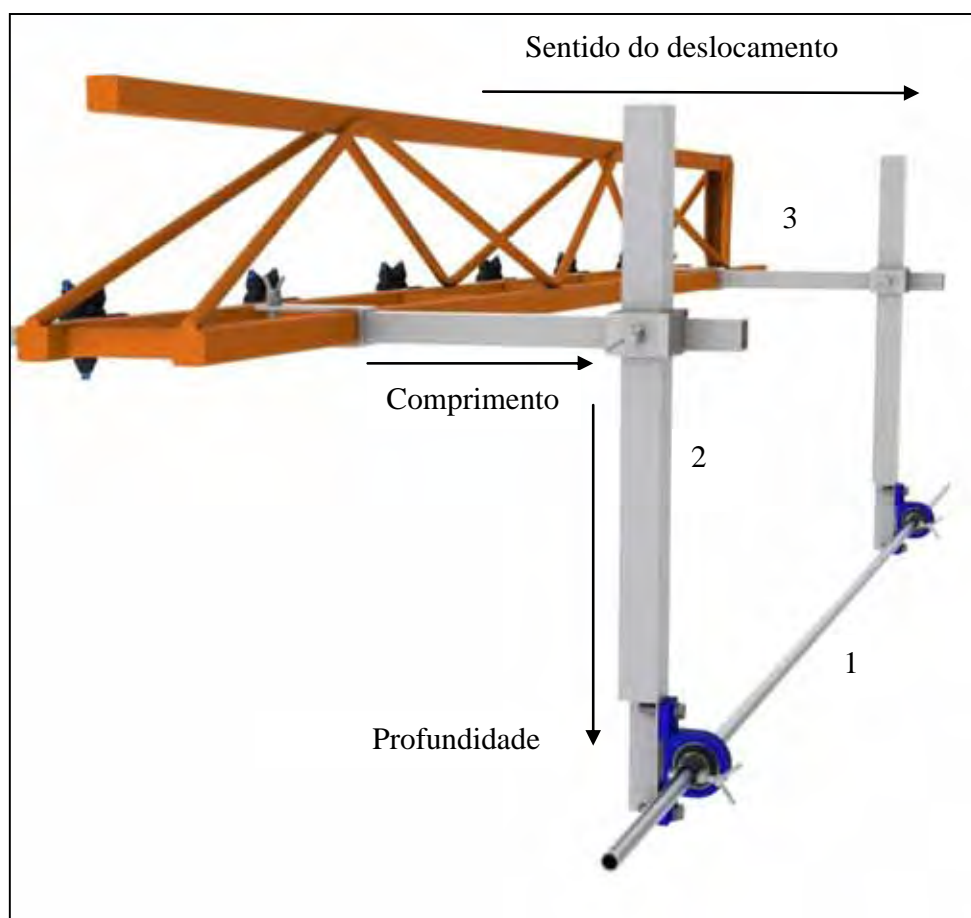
Representação esquemática do dispositivo *CO* demonstrando o comprimento e a profundidade entre a barra tubular de ferro e as pontas de pulverização. 1- barra tubular de ferro; 2- suporte vertical; 3- barra horizontal. Botucatu-SP, 2012.
